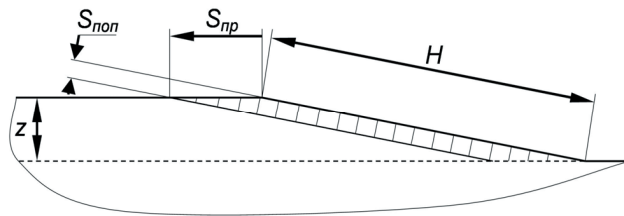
Схема съема припуска при бесцентровом шлифовании со скрещивающимися осями инструмента и детали
